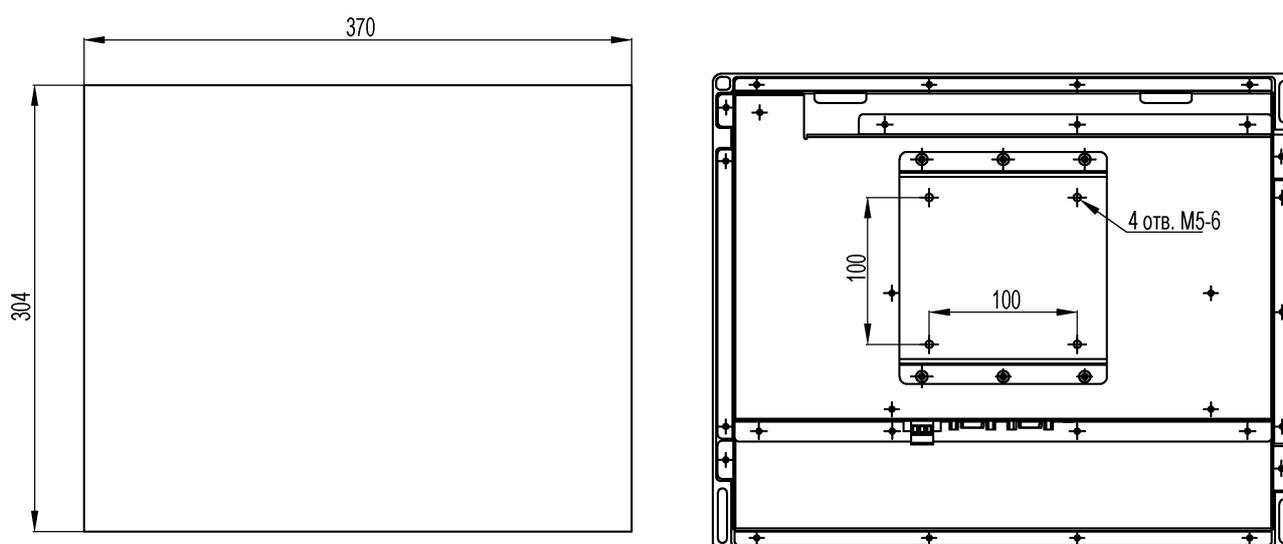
Габаритные и установочные размеры панели ETC-250-EMH-101-0000
